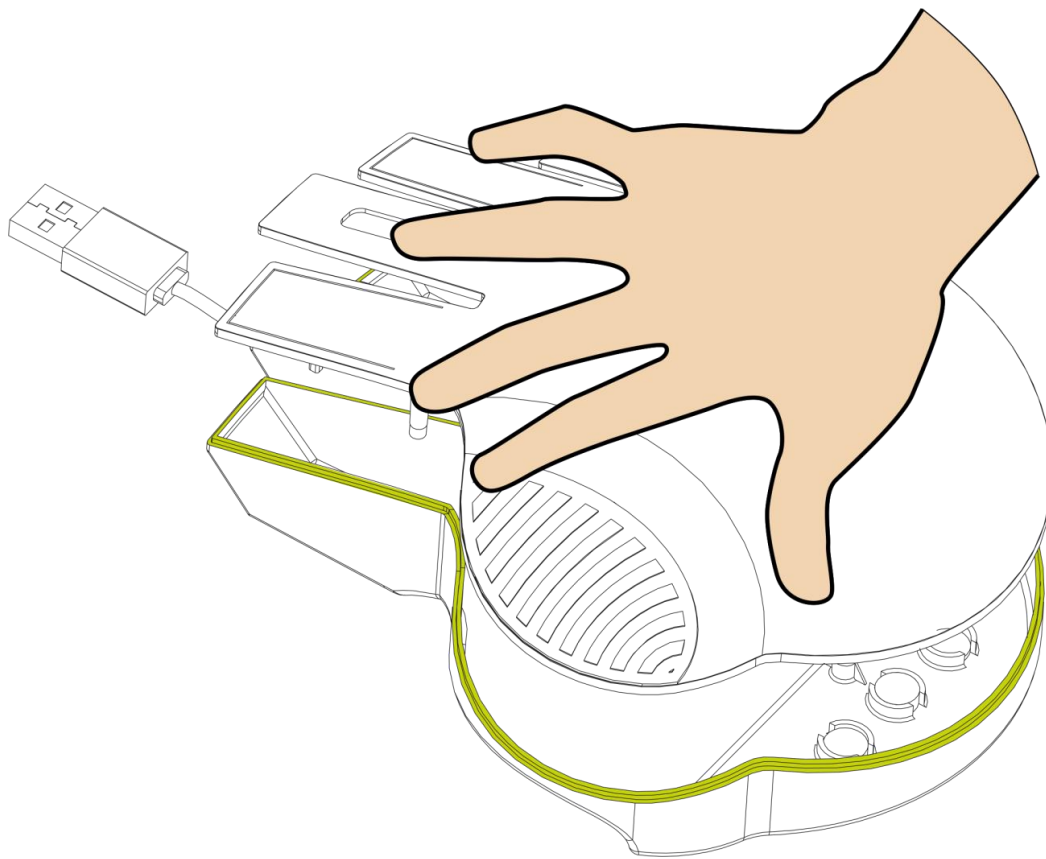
Ensamblaje 2 – 1 (1)
